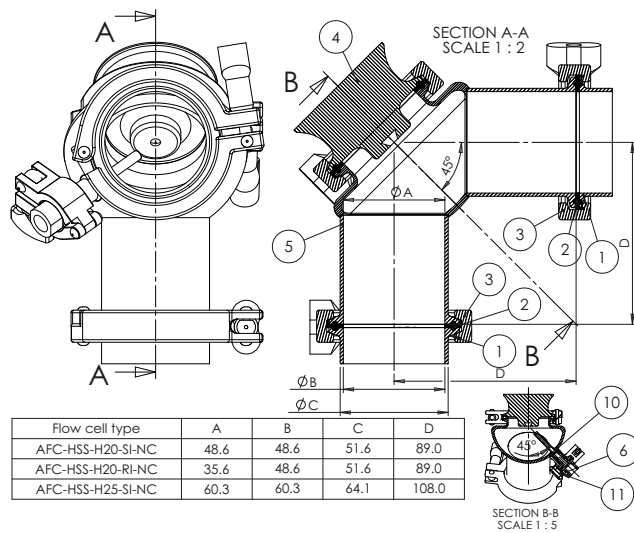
Cuve de circulation AFC-HSS-avec raccordement au gicleur de lavage (-NC) H20 pour tube de 2 pouces (50 mm) de diamètre et H25 pour tube de 2,5 pouces (65 mm) de diamètre
